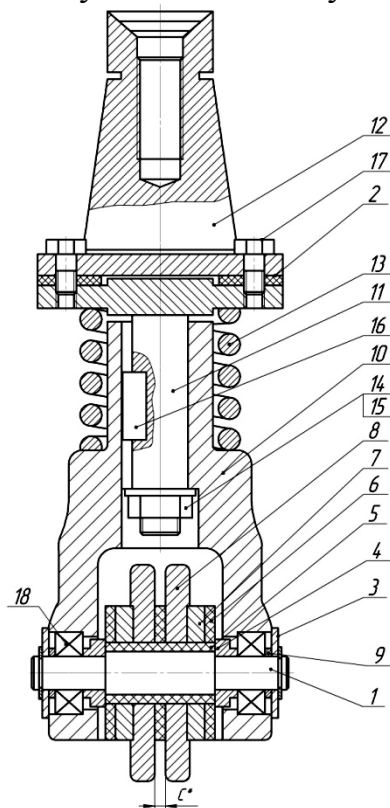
Загальний вид нового пристосування для ЕМО:
